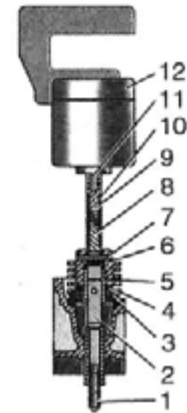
Приспособление для шлифовки седел клапанов:
